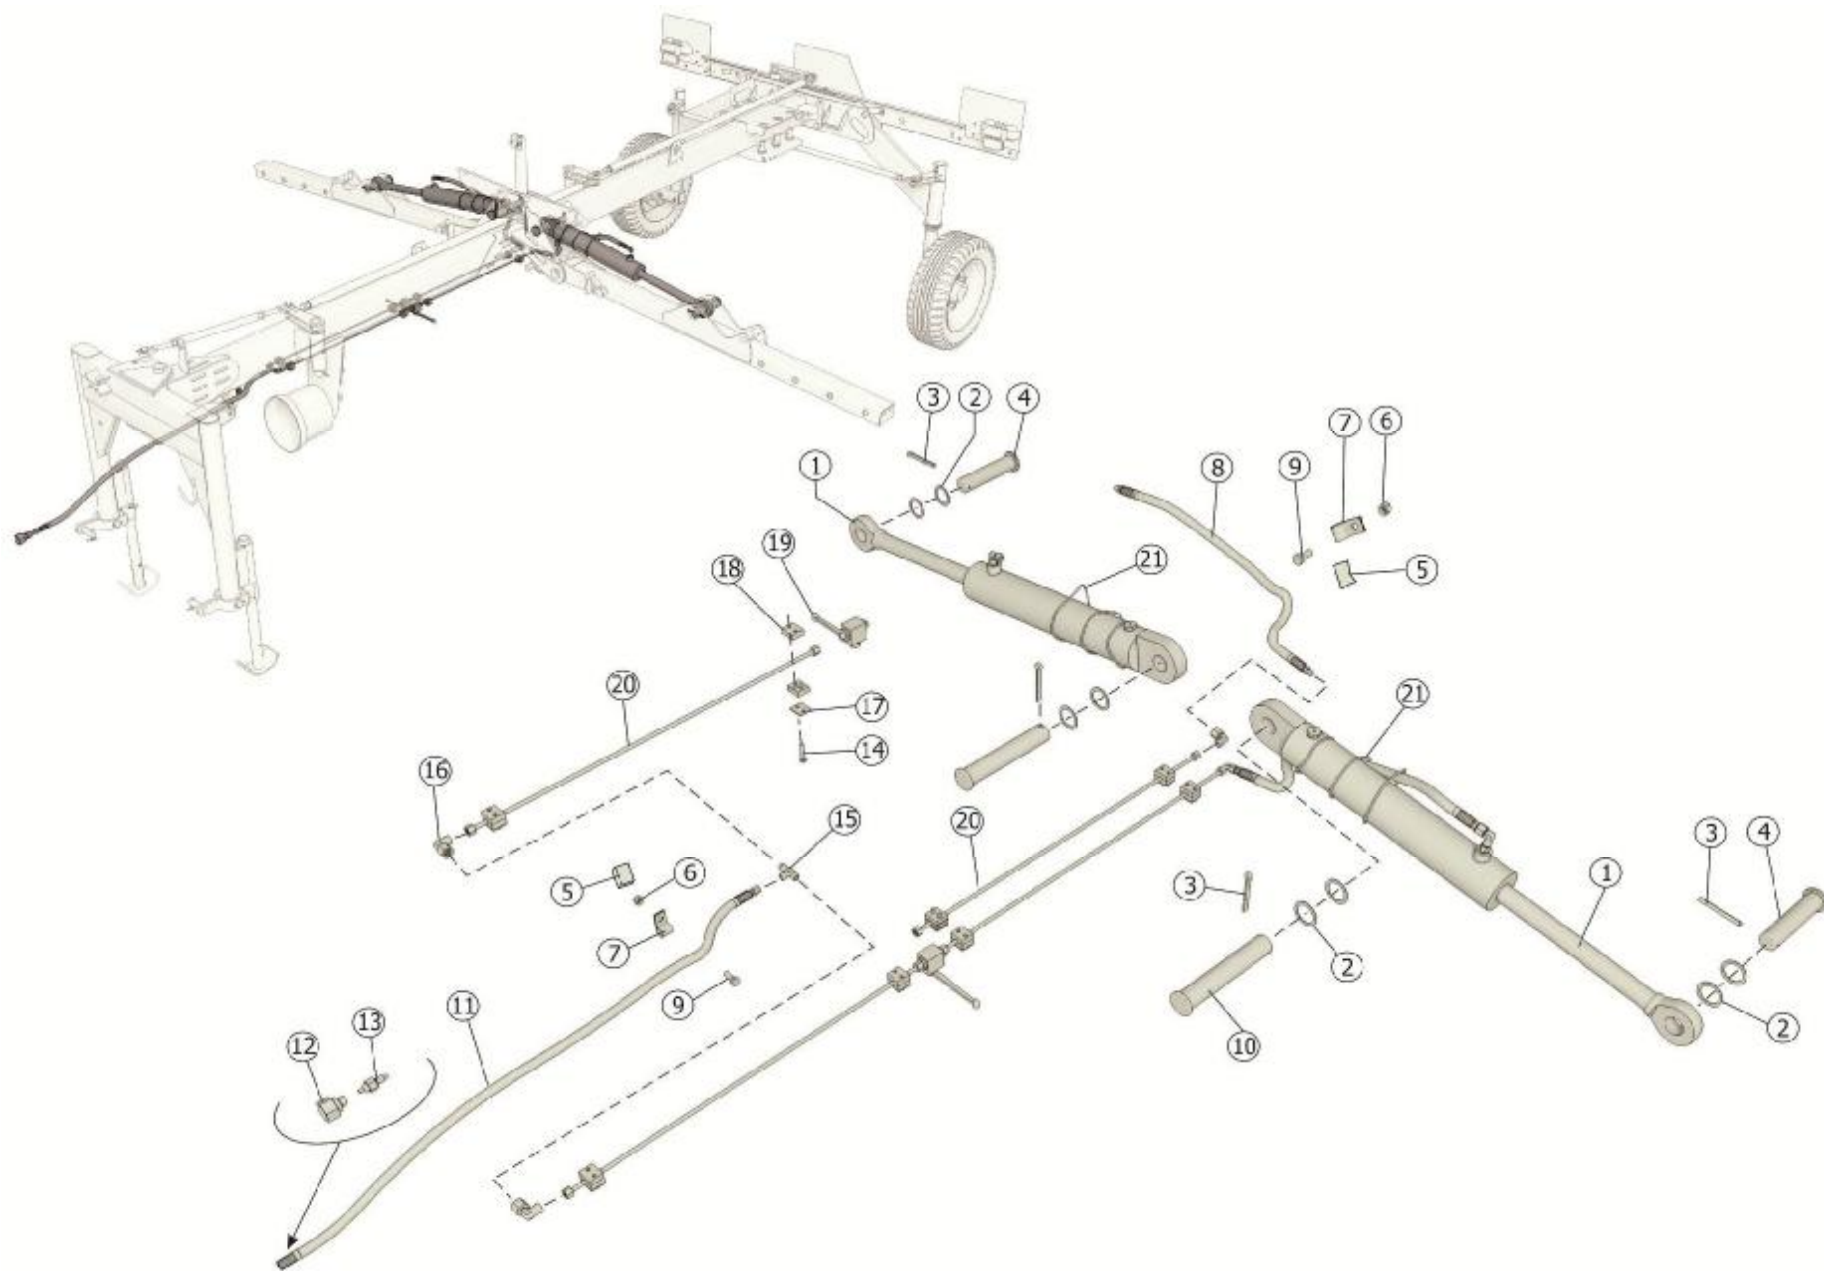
Установка гидрооборудования ГРП-811.09.00.000
